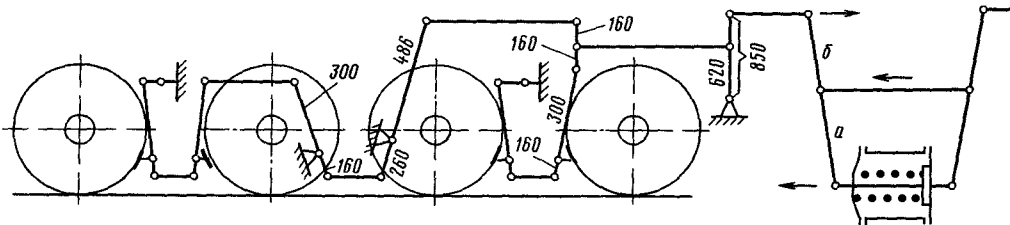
Схема рычажной передачи тележки восьмиосной цистерны
